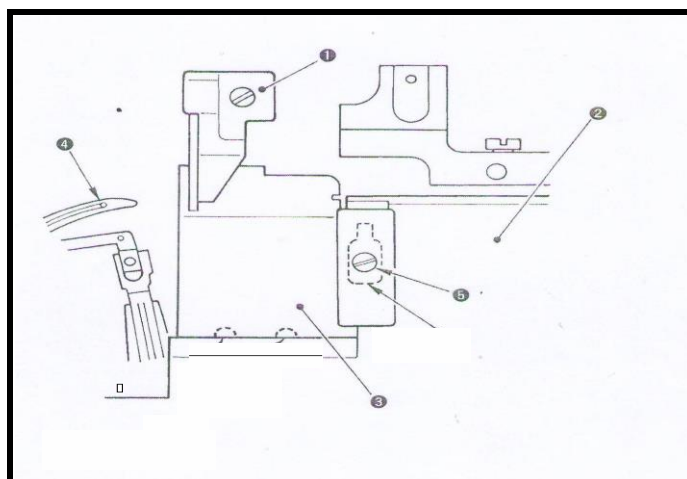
Предохраняющая пластина. 1-верхний нож, 2-крышка переднего петлителя, 3- предохраняющая пластина, 4- нижний петлитель, 5- винт.
